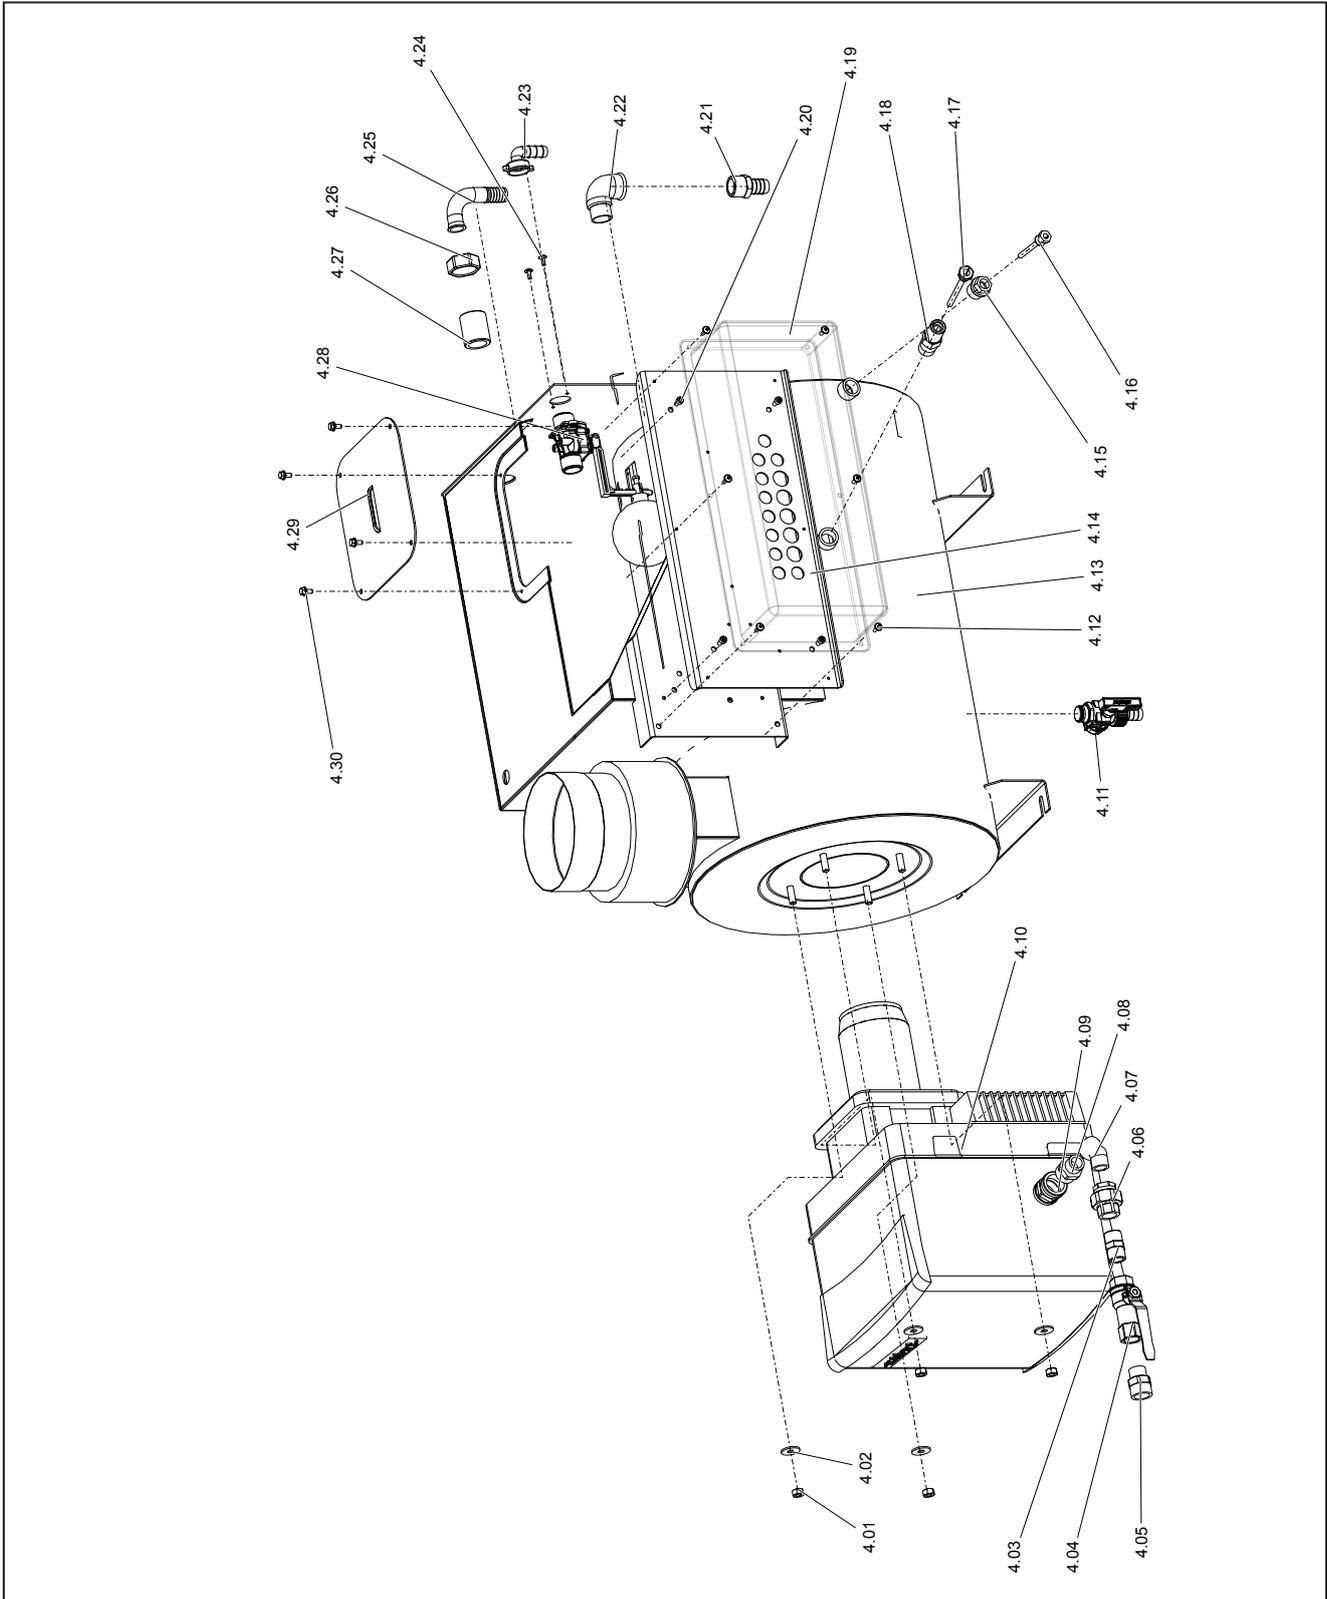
4 Weißhaupt Gasbrenner mit Boilersystem, Explosionszeichnung
